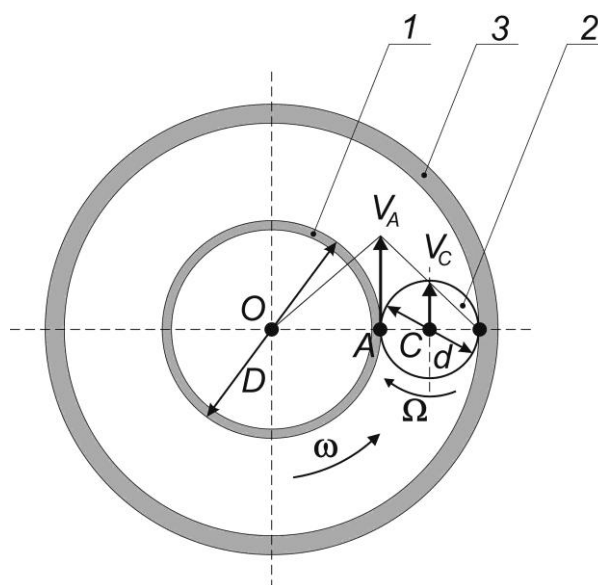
Схема радиального подшипника качения: 1 – внутреннее подвижное кольцо; 2 – тело качения; 3 – наружное неподвижное кольцо.
